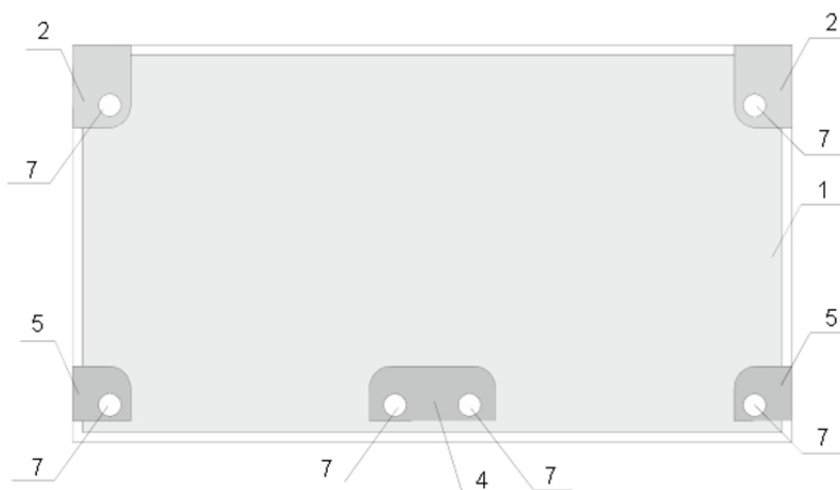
Модернизированный стол для укладки заготовок с базирующими элементами
